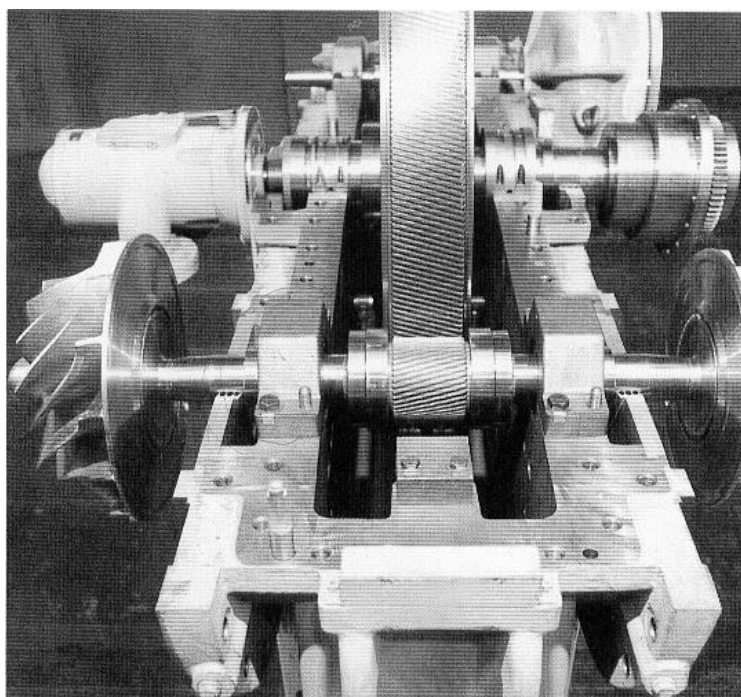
б. Вид на быстроходный и тихоходный роторы многовального центробежного компрессора (корпуса ступеней и верхняя крышка корпуса повышающей зубчатой передачи сняты)
